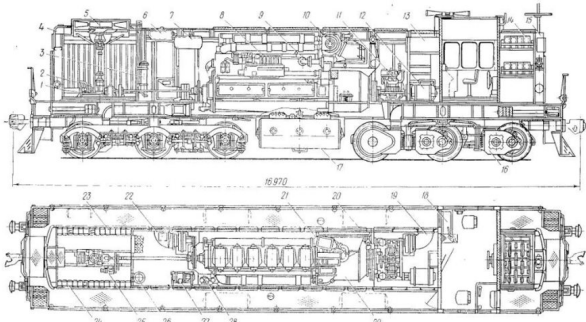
Растворительное оборудование на тепловозе ТЭМ2
